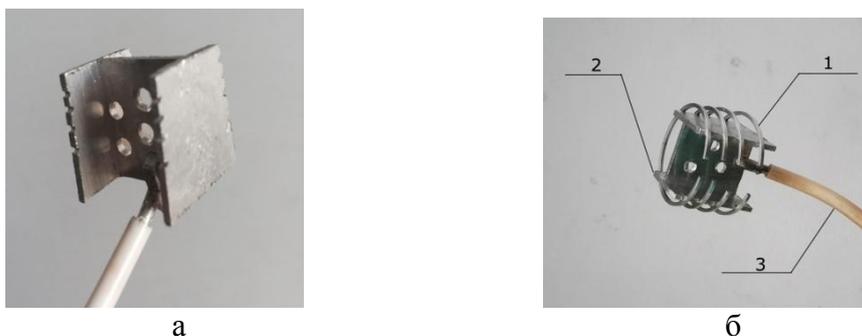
Приспособление для поршневых колец: а – внешний вид приспособления; б – приспособление с кольцами: 1-поршневые кольца; 2 – приспособление; 3 – алюминиевый провод
